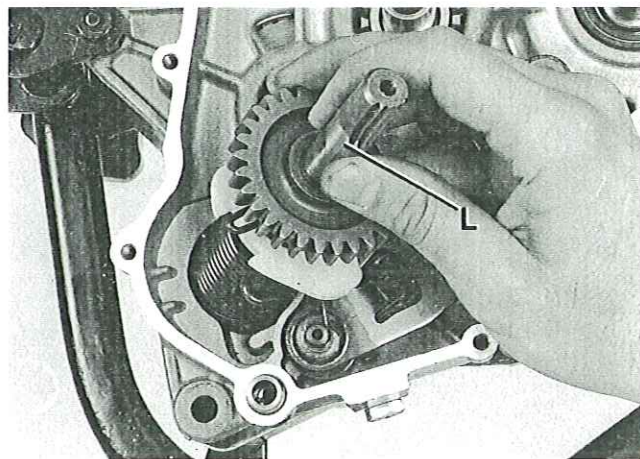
Engranaje libre, engranaje eje equilibrado y engranajes de transmisión
